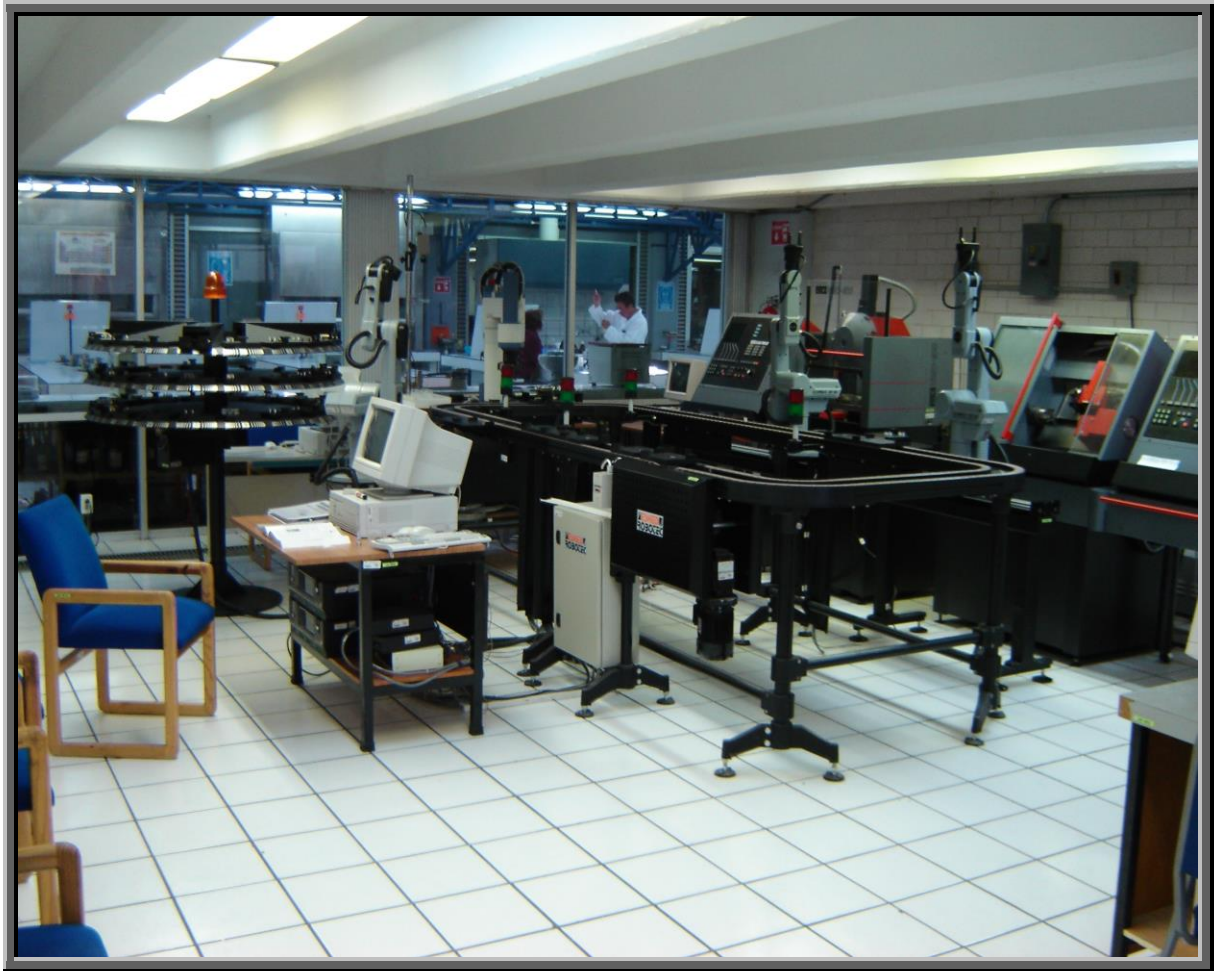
Vista del Aula de manufactura lado izquierdo CIM, Torno y Fresadora.
